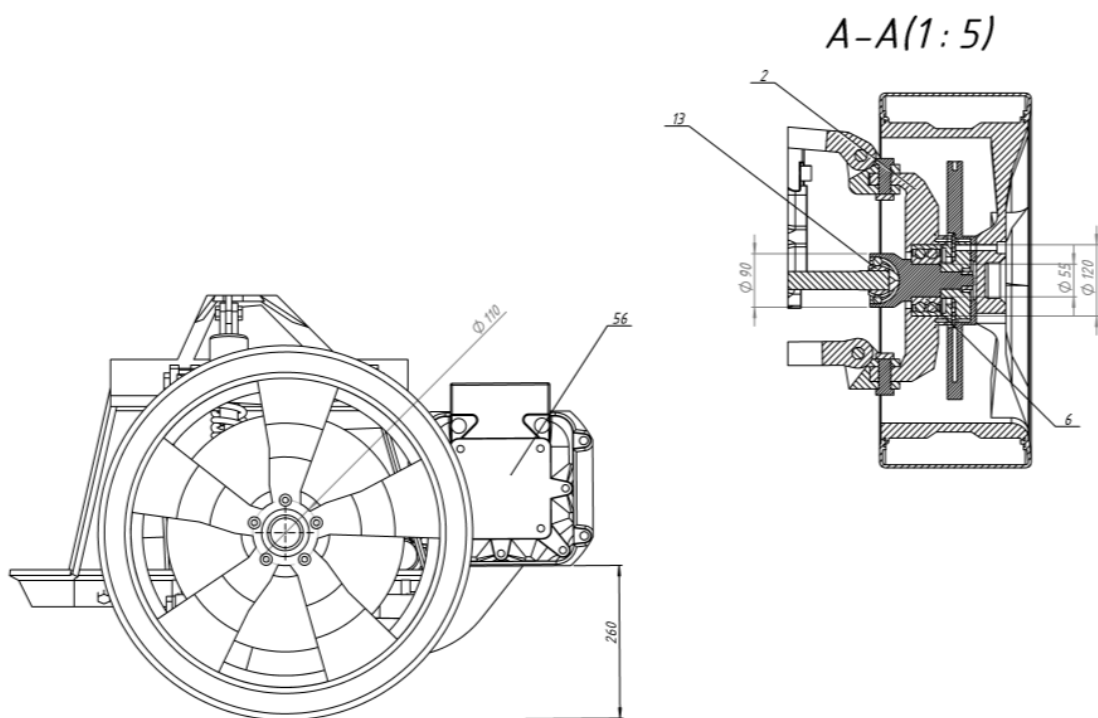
Загальний вигляд переднього приводу (Вид зліва та Розріз А-А)
